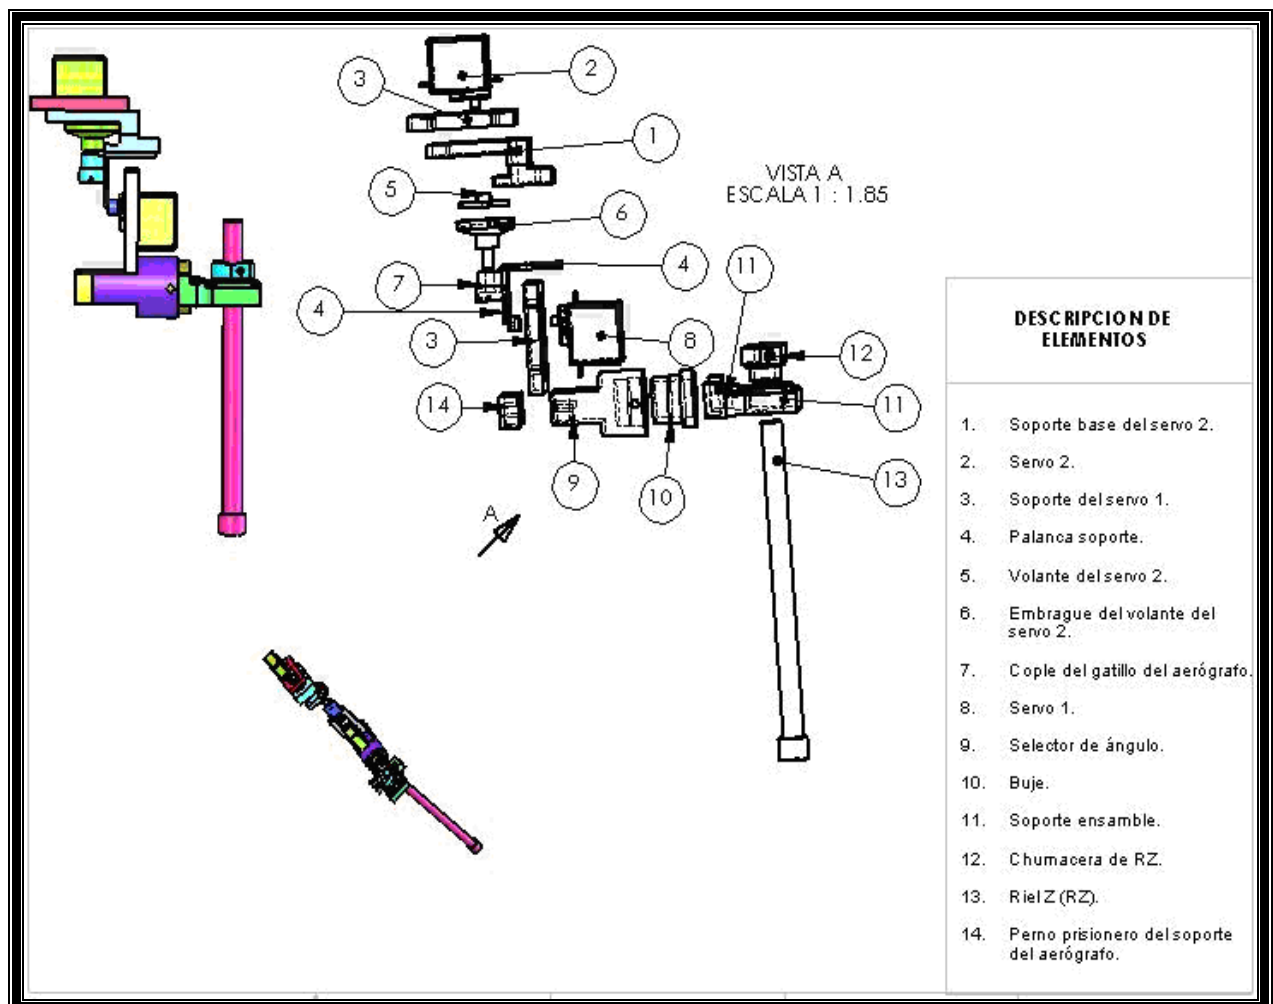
Vista explosionada del ensamble de mecanismo terminal.
